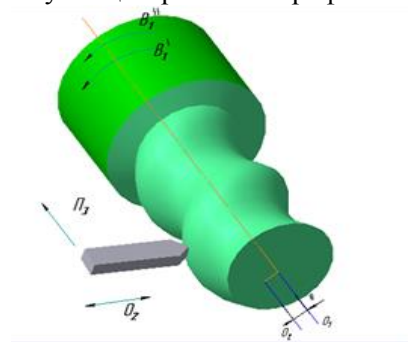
Кинематические схемы обработки круговых винтовых поверхностей на токарно-затыловочном станке
